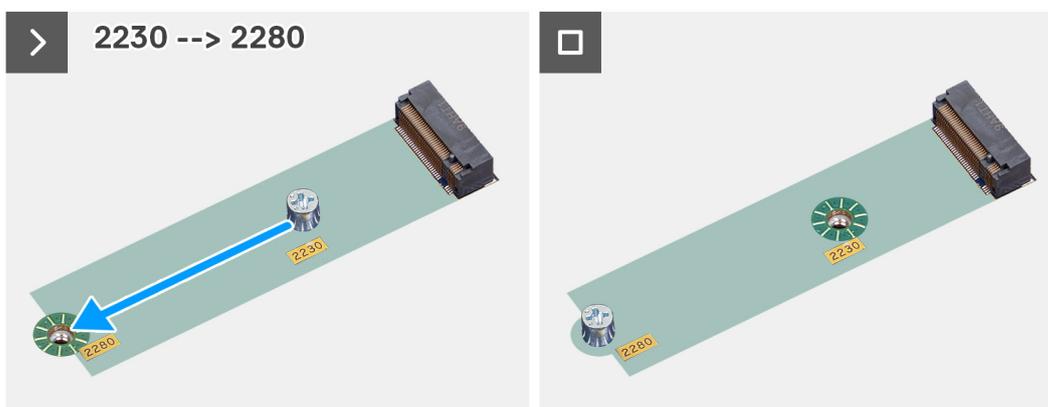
Befestigen der Schraubenhalterung von 2230 auf 2280
